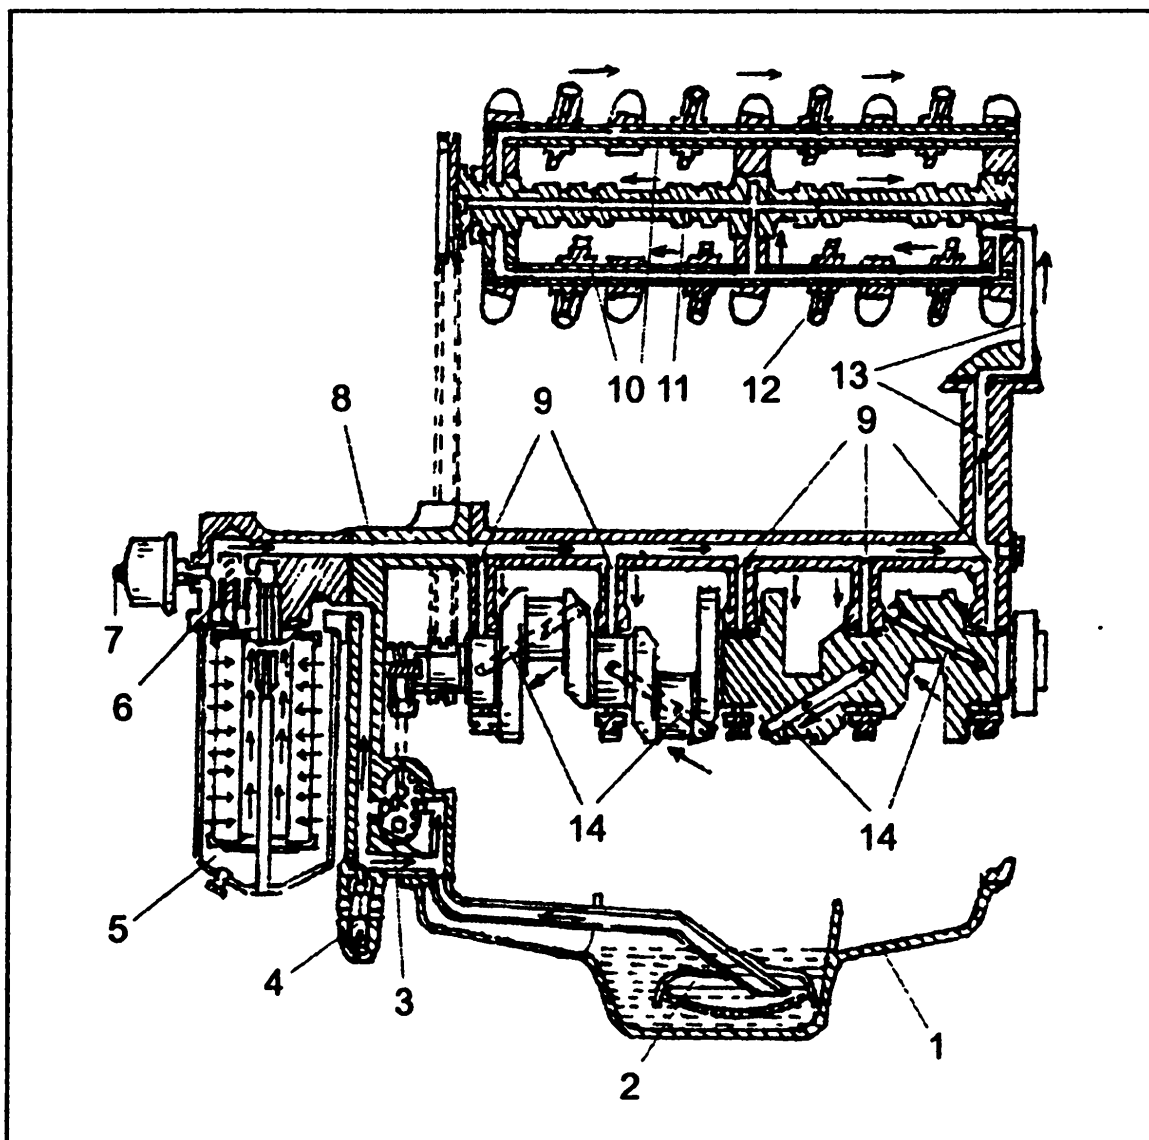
Принципиальная схема устройства и работы системы смазки двигателя:
